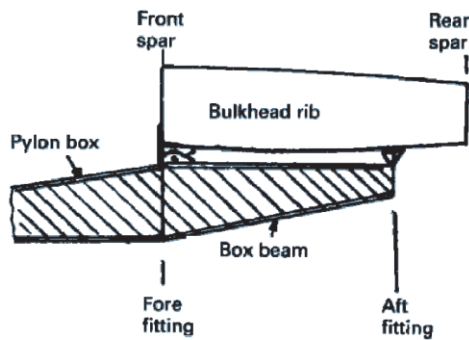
Triebwerksaufhängung in Kastenbalken-Konfiguration (nach Niu 1999, aus Airframe Structural Design)
